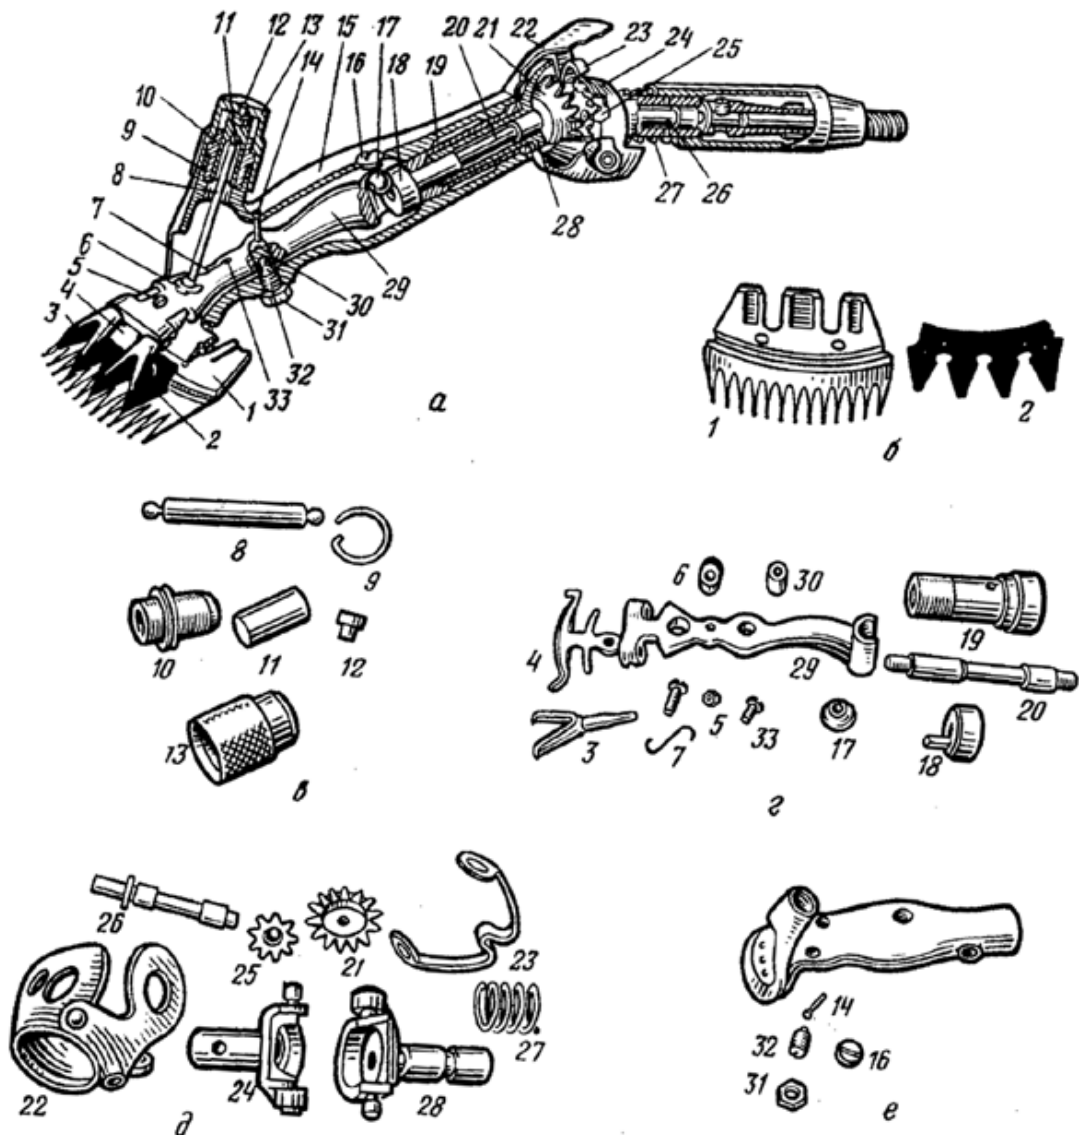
Загальний вид (а) машинки МСО-77Б для стрижки овець і деталі ріжучого апарата (б), притискного (в), ексцентрикового (г), шарнірного(д), механізмів і корпуса (в);
